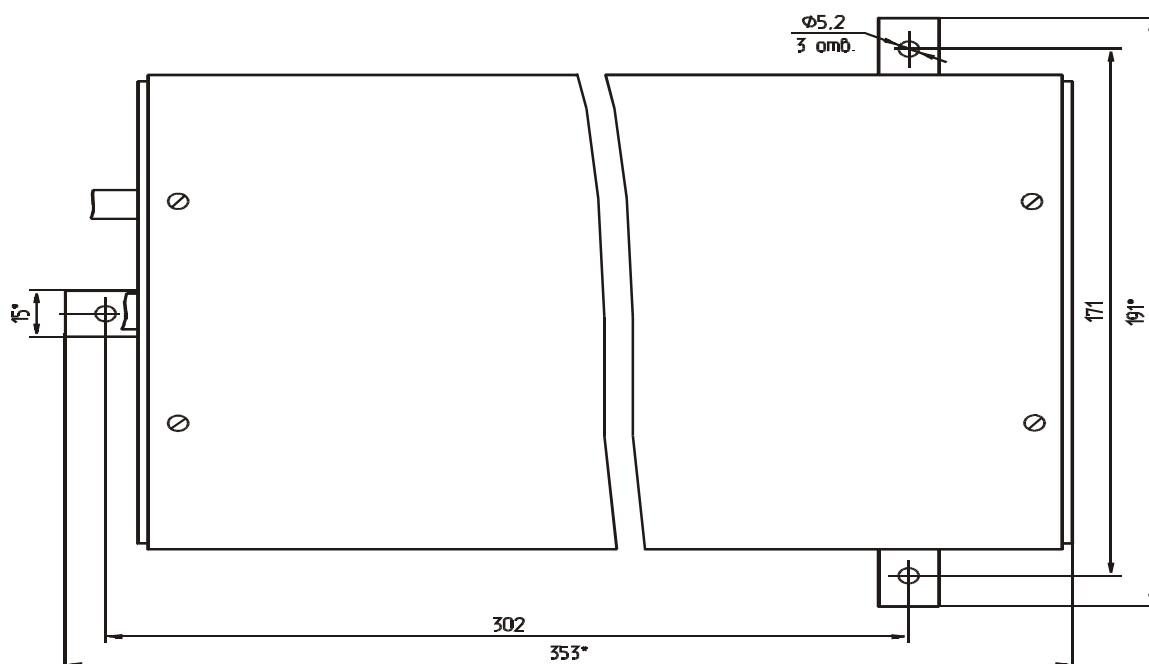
Габаритные и присоединительные размеры БПВРа
